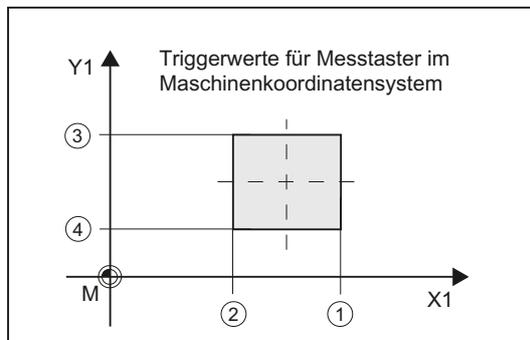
Werkzeugmesstaster, maschinenbezogen (G17)
